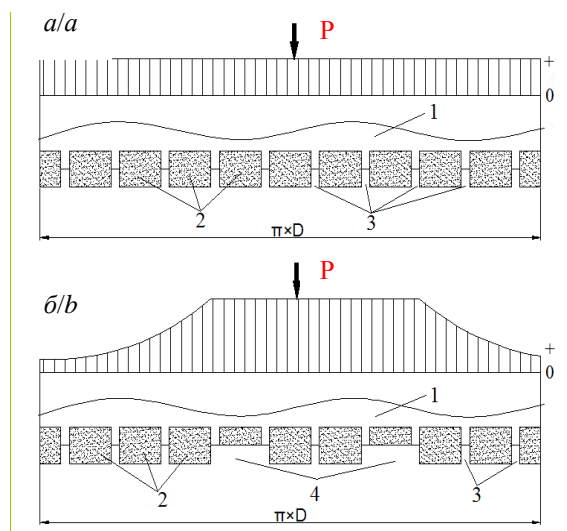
Развертка боковой поверхности коронок: а) стандартной коронки; б) испытываемого образца коронки КИТ; 1 – корпус; 2 – сектора; 3 – малые промывочные каналы; 4 – большие промывочные каналы
